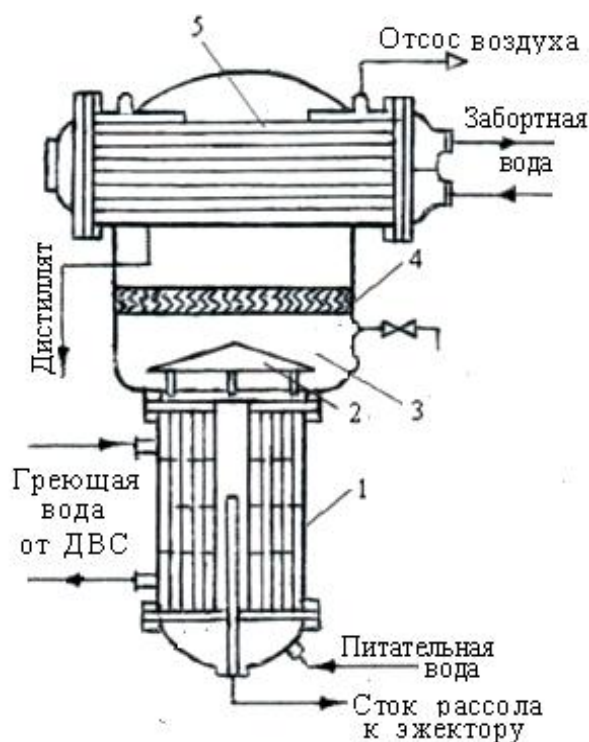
Конструктивная схема и общий вид утилизирующего опреснителя типа «Д»:
